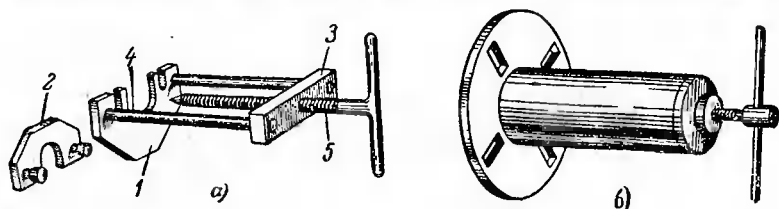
Съемники для шариковых и роликовых подшипников.
